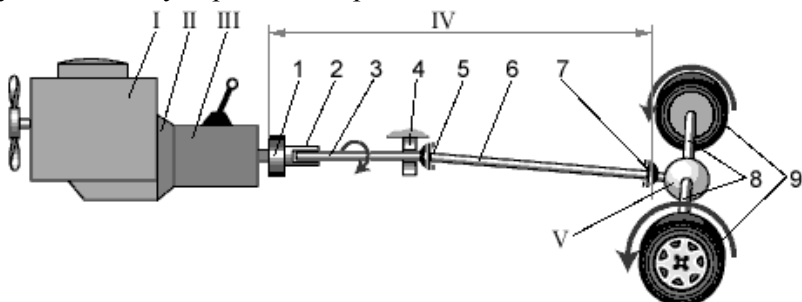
Схема трансмиссии заднеприводного автомобиля I - Двигатель; II - Сцепление; III - Коробка передач; IV - Карданная передача: 1 - эластичная муфта; 2 - шлицевое соединение; 3 - передний карданный вал; 4 - подвесной подшипник; 5 - передний карданный шарнир; 6 - задний карданный вал; 7 - задний карданный шарнир; V - Задний мост с главной передачей и дифференциалом: 8 - полуоси; 9 - ведущие (задние) колеса
